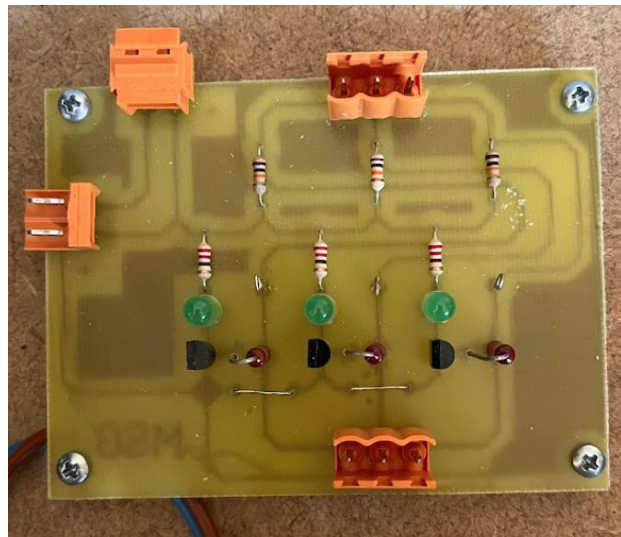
PCB de acondicionamiento de los sensores de efecto Hall. Fuente [Propia]
